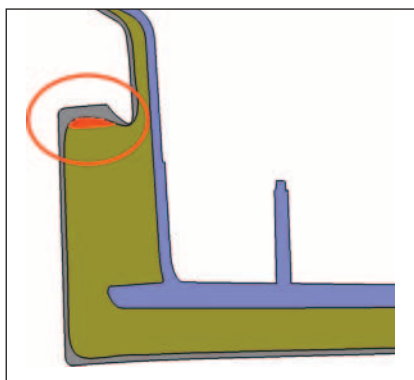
Querschnitt durch ein Werkzeug mit Liftertechnik für Türbrüstungen
